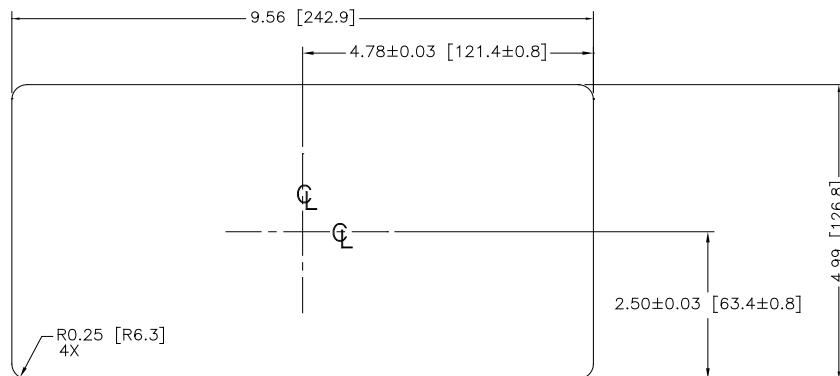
Dimensões do gabinete do IND560 em corte para montagem em painel
